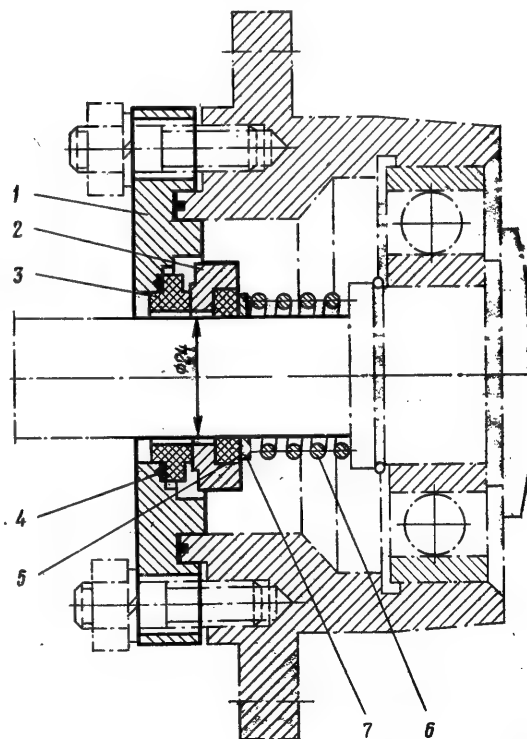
Сальник пружинный уплотнения вала с кольцами трения (компрессор ФВ6):
